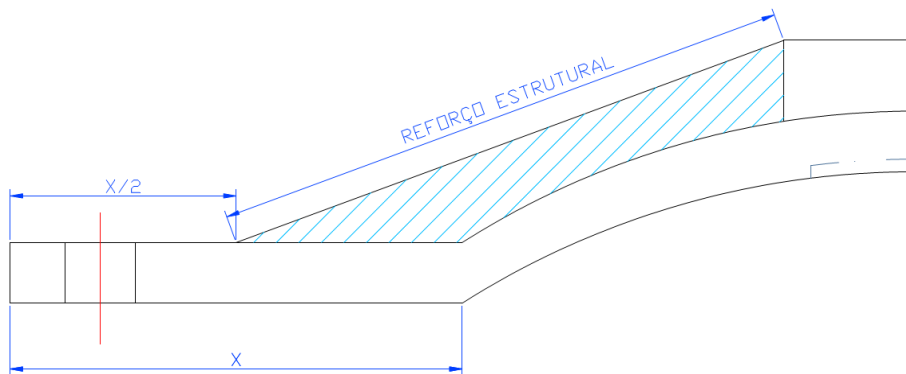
Desenho esquemático do detalhe do reforço estrutural para abraçadeiras
